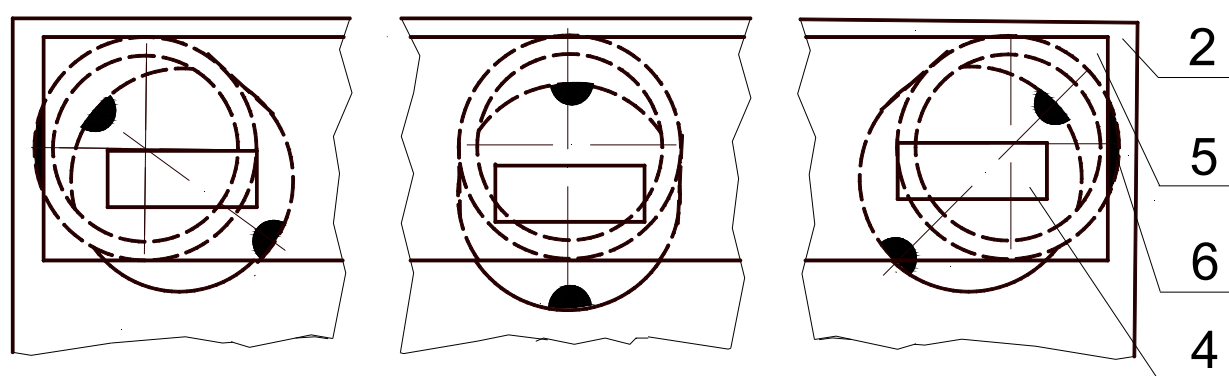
Збірна робоча пластина з розміщеними в середині кусками металу жертвовного аноду.
